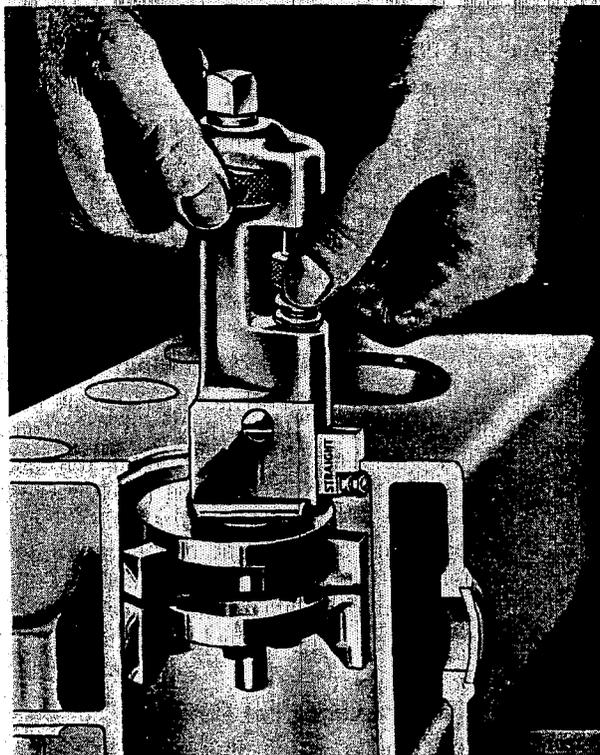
Werkzeug für das Abtragen der Zylinderränder
